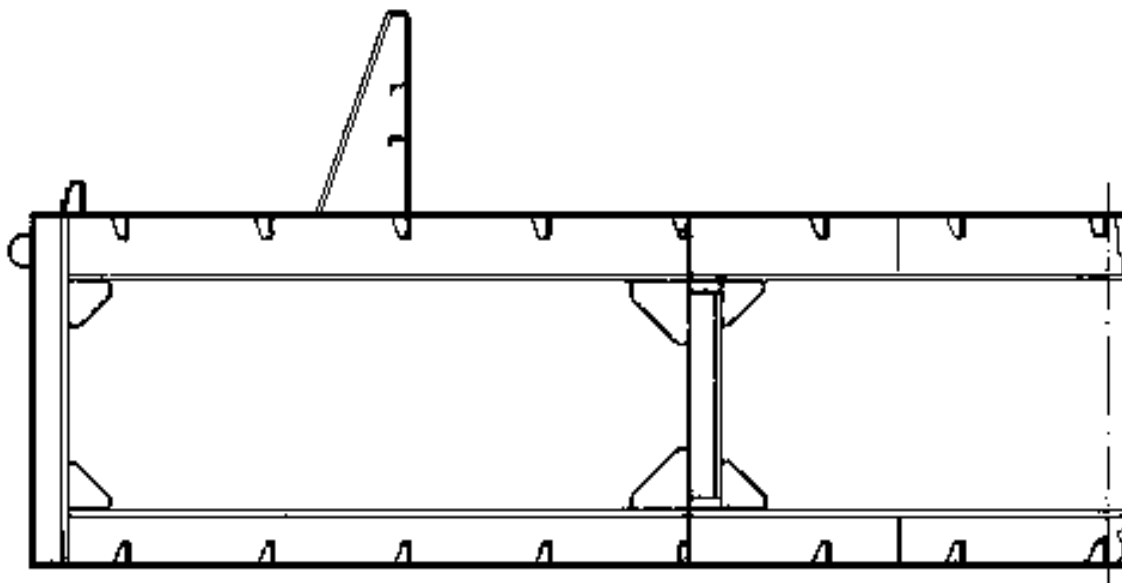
Мидель-шпангоут баржи – площадки пр. 81210 /8/
